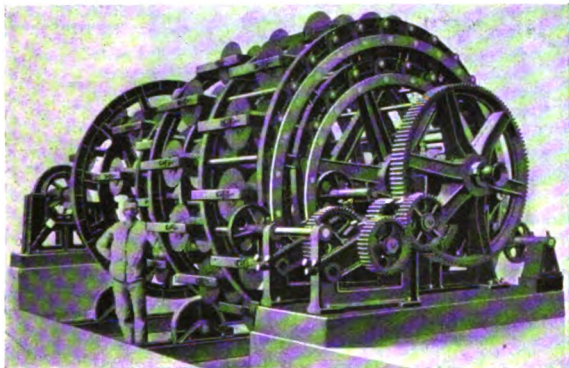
Versellkorb einer Bewehrungsmaschine für Rund- und Flachdrähte.
